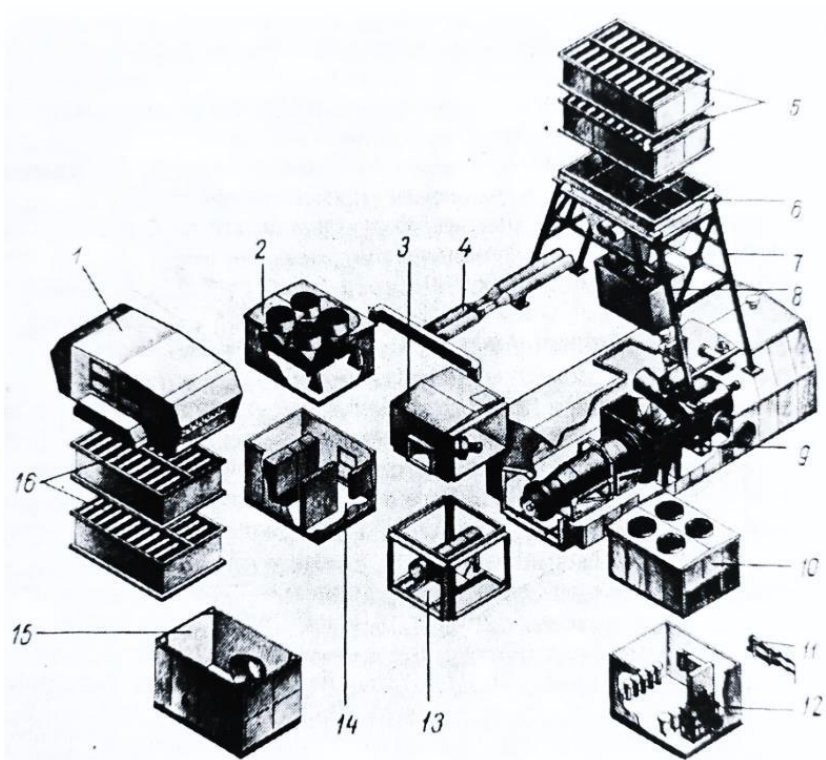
Блоки агрегата типу ГПА-Ц-16:
